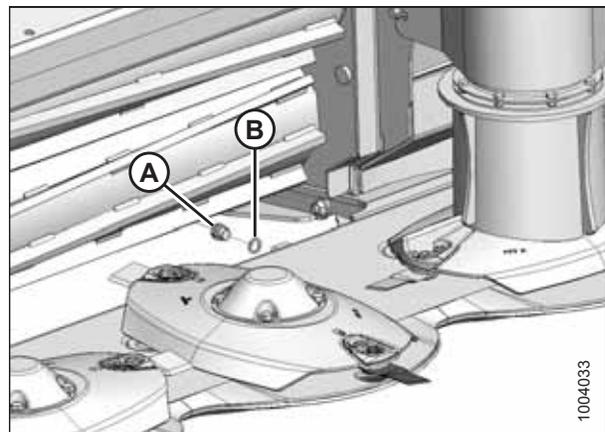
Bouchon d'inspection d'huile de barre de coupe
